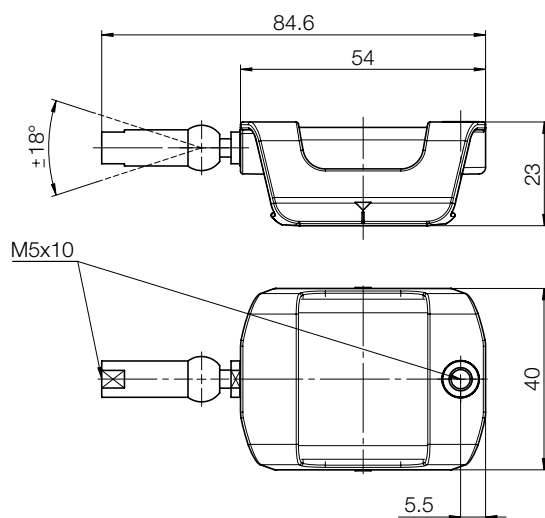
Medidas de montaje de los sensores de posición BAM TG-IR-037-A
